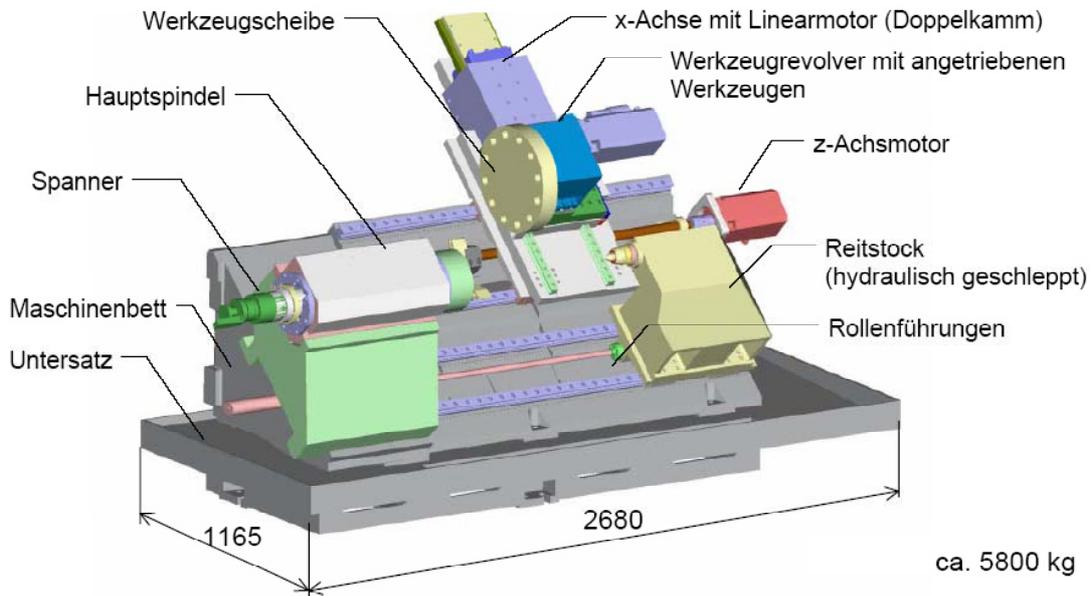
Bauelemente einer Drehmaschine in Bettbauweise (Quelle Gildermeister)
